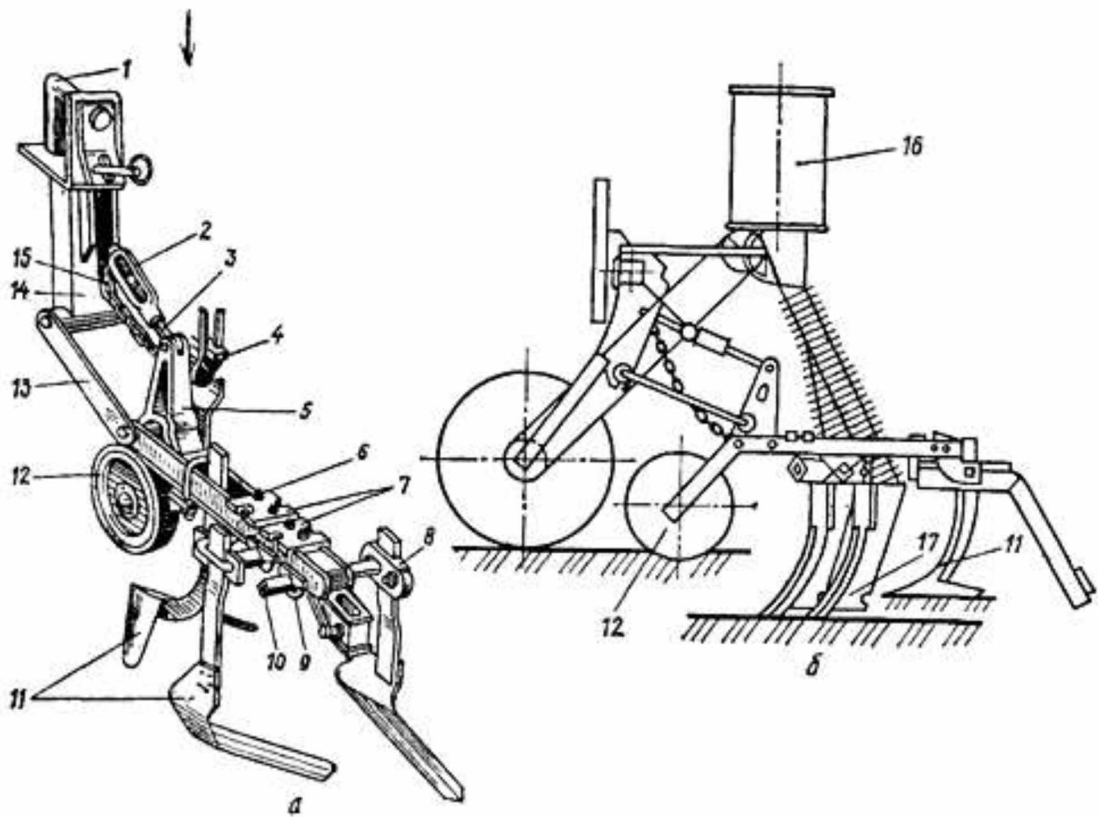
Секція робочих органів культиватора КРН-5,6Б (а) і схема культиватора з підживлювальним пристроєм (б): 1 — скоба; 2 — стяжна гайка; 3 — верхня ланка; 4 — важіль регулятора глибини; 5 — задній кронштейн; 6 — гряділь; 7 — накладки; 8 — тримач лапи; 9 — призма; 10 — брус; 11 — лапи; 12 — копіювальне колесо; 13 — нижня ланка підвіски; 14 — передній кронштейн; 15 — ланцюг; 16 — туковисівний апарат; 17 — ніж підживлювач[8].
